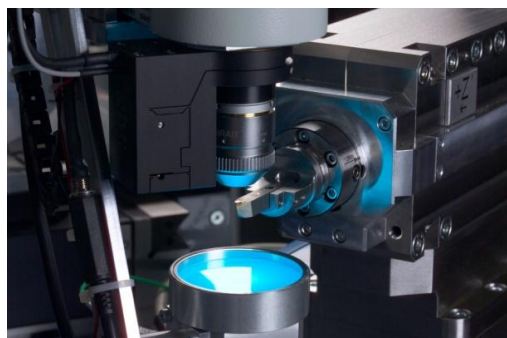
In die Bearbeitungsmaschine integriertes hybrides Messsystem
